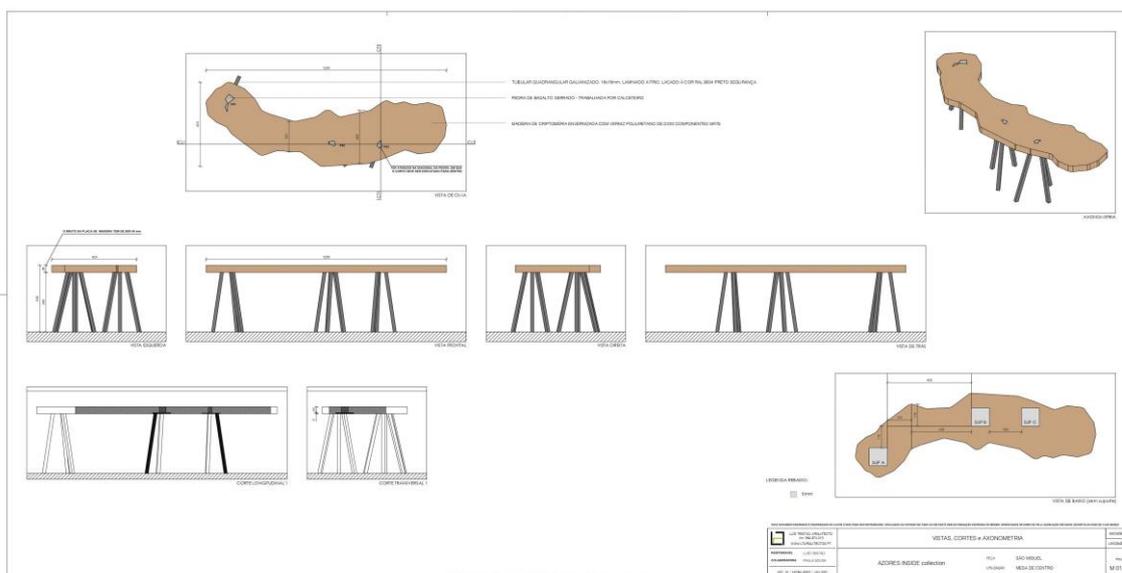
Desenho técnico da ilha de São Miguel: vistas, cortes e axonometria.
